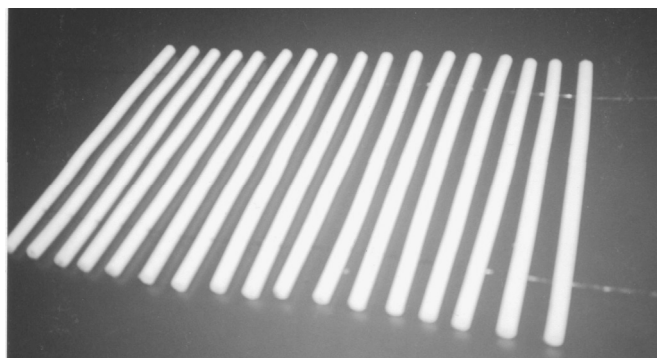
Формовочный корсет с нажимными элементами из фторопласта-4
